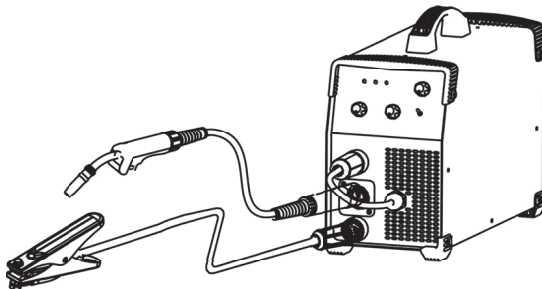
Схема подключения для сварки в среде защитных газов
